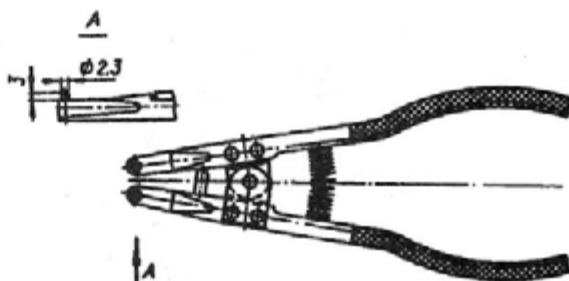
Круглогубцы для снятия и установки стопорного кольца крепления рабочего цилиндра в картере сцепления
